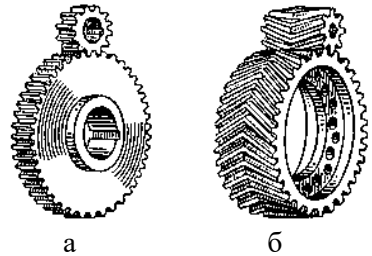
Зубчасті колеса: а – прямозубі; б – шевронні
